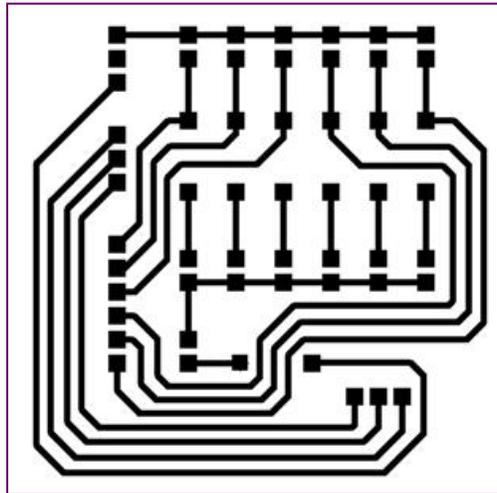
Esquema del circuito impreso elaborada en PCB Wizard.
